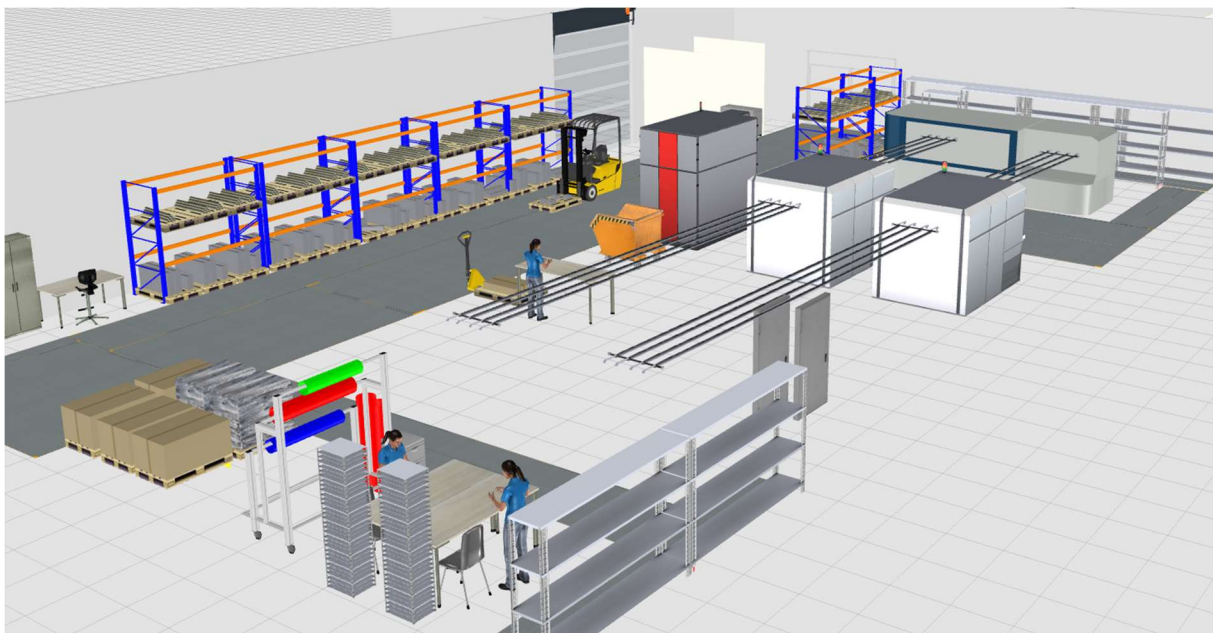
2D layout navrhovaného uspořádání skladovacích prostorů ve výrobní hale
